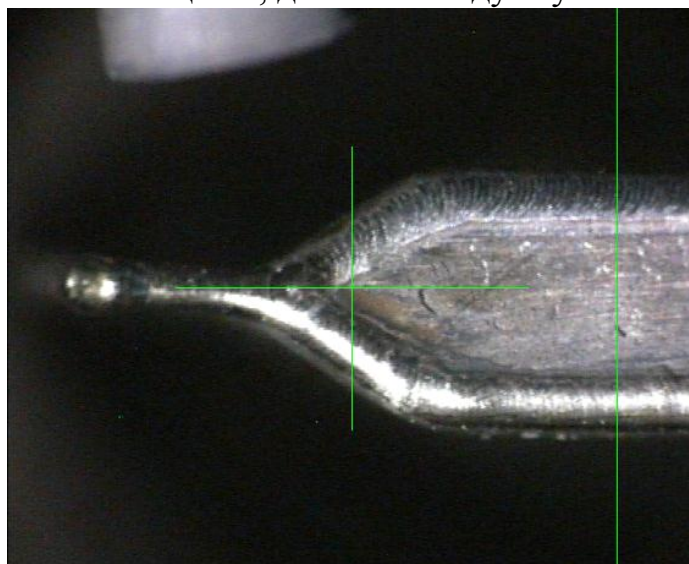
Сварное соединение изделий разной толщины
